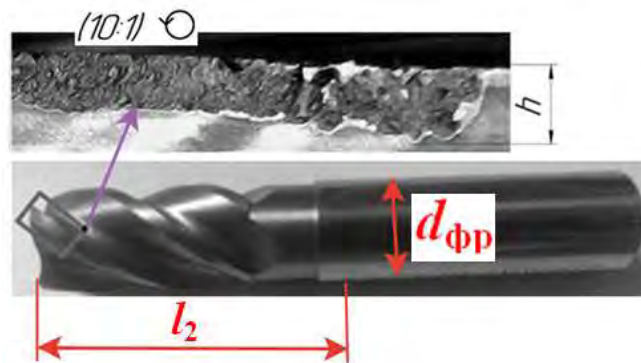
Длина фаски износа  $h$  по задней поверхности главной режущей кромки концевой фрезы
